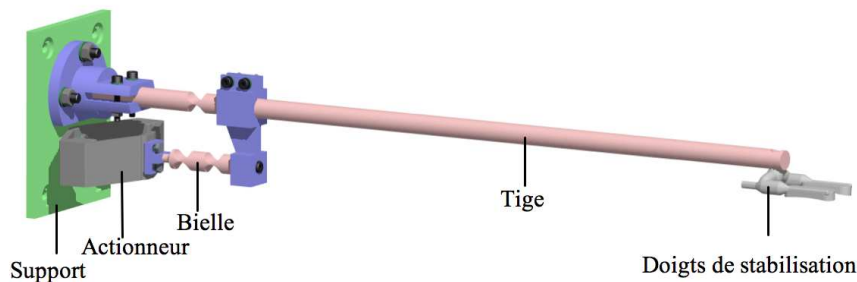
Vue générale CAO du dispositif Cardiolock 1
